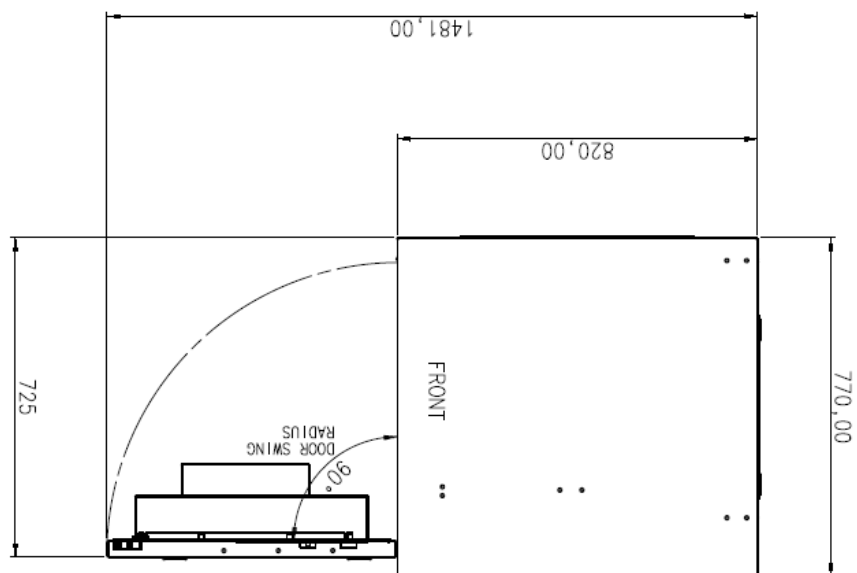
Зазоры шкафа, вид сбоку и вид сверху
